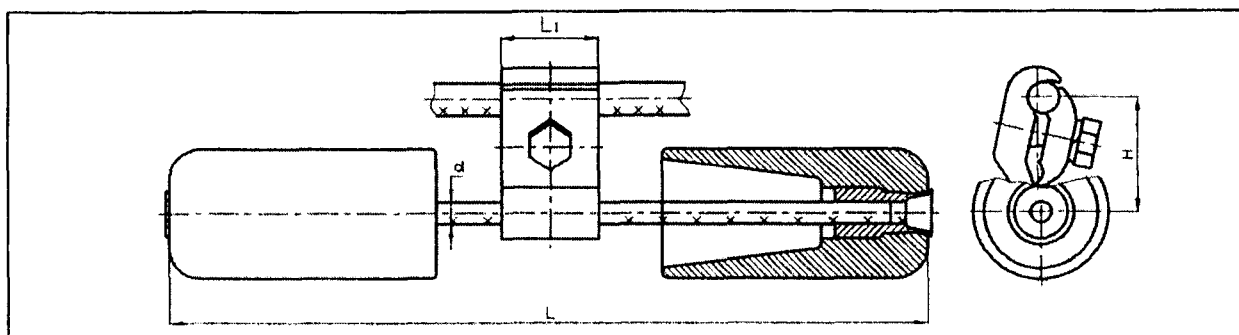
Внешний вид, конструкция и размеры гасителя вибрации типа ГПГ-В
